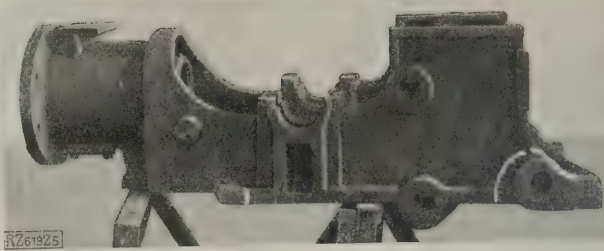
Warmgeschweißter Maschinenrahmen (Grauguß).
